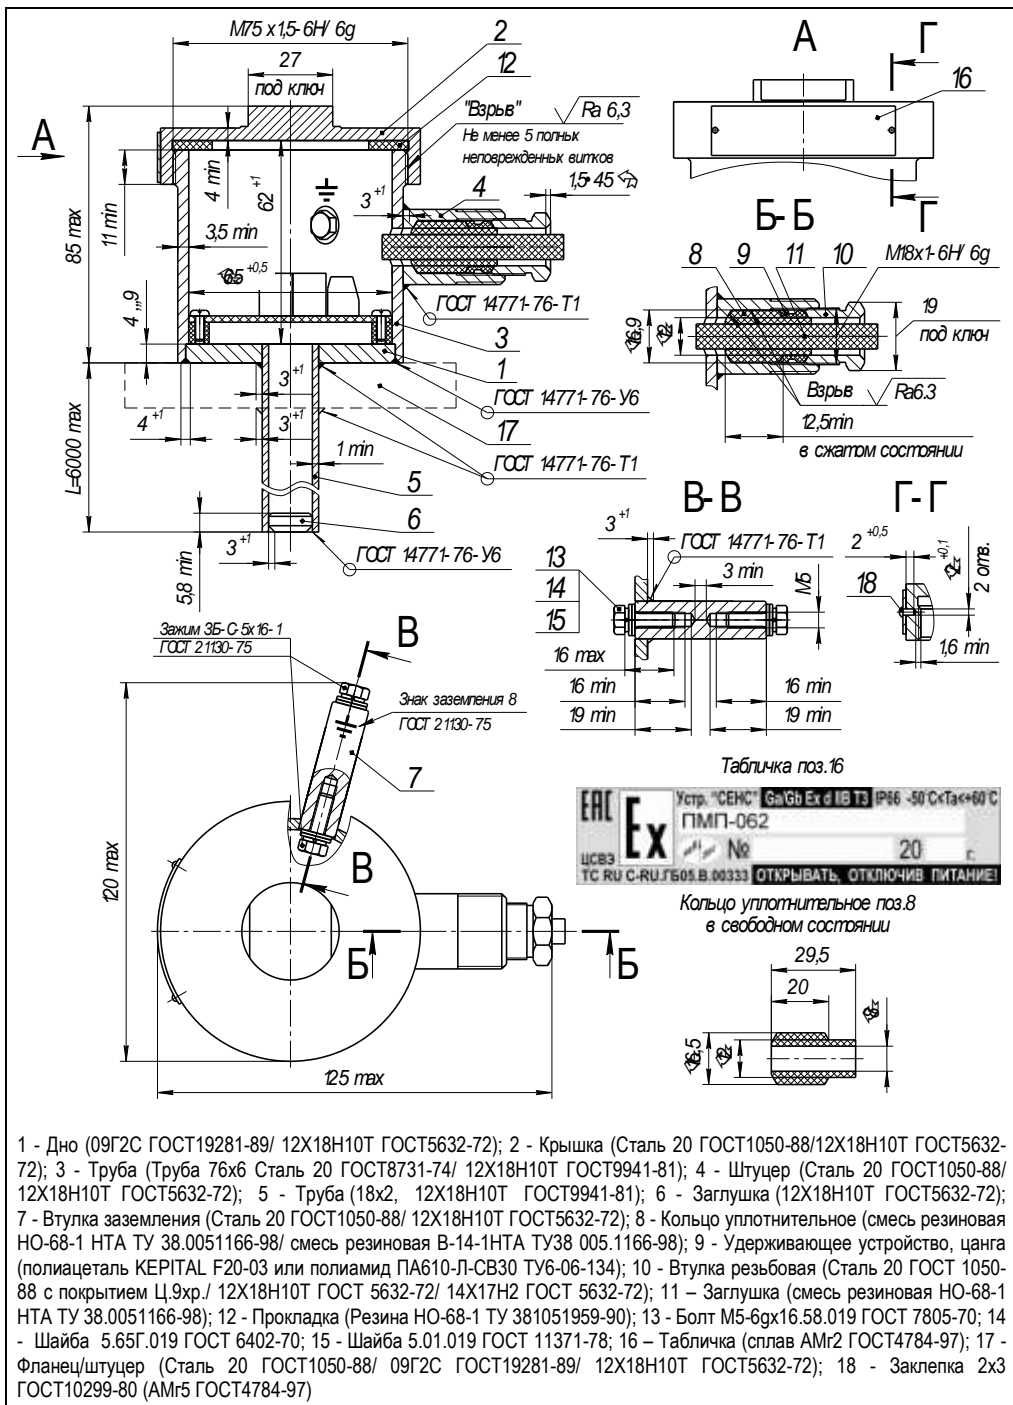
Чертеж средств взрывозащиты для преобразователя со сварным корпусом
